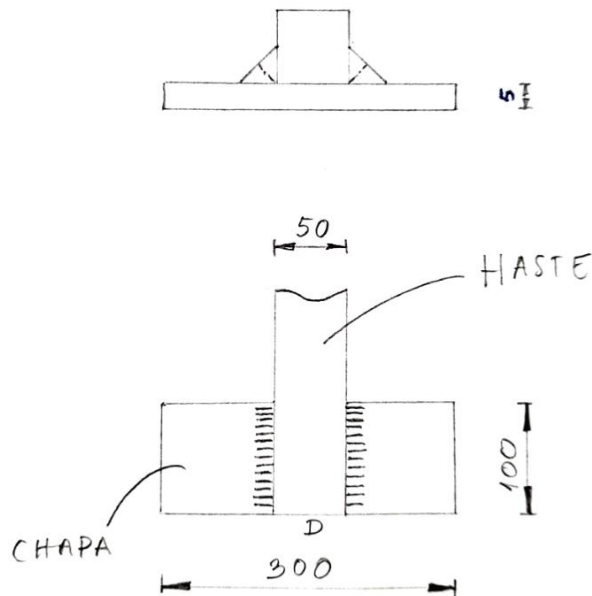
Esboço da soldadura entre as chapas e a haste.
